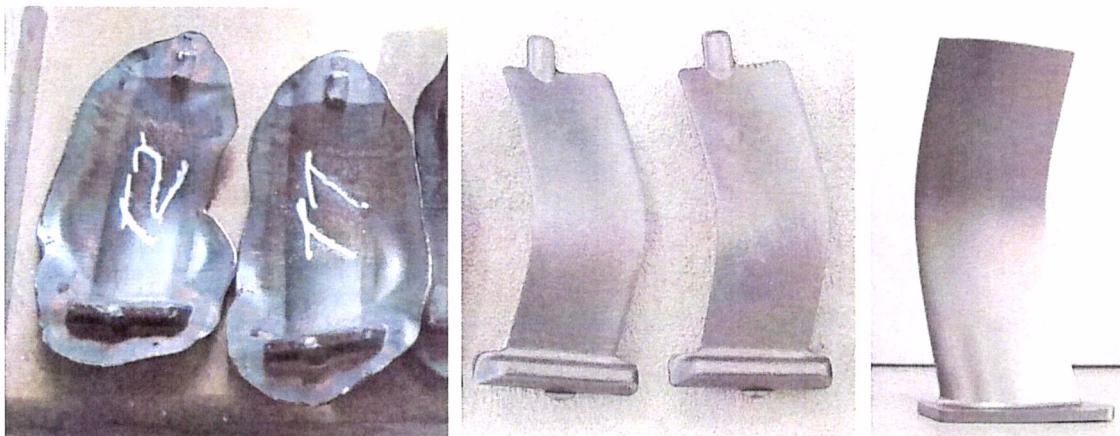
штамповки лопаток, штамповки лопаток после обрезки облоя, обдувки и травления, лопатка, полученная после механической обработки гибридной штамповки.
